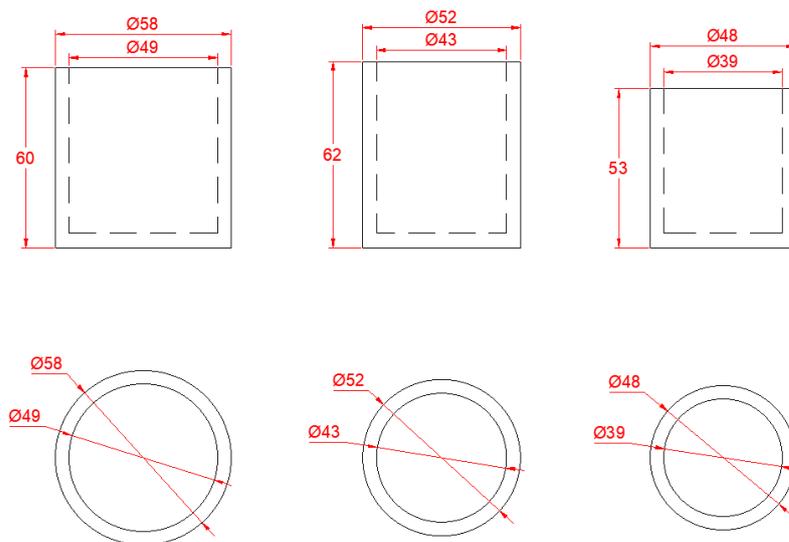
Alzado y planta de los tres pistones y sus dimensiones (en mm). Fuente: elaboración propia.
